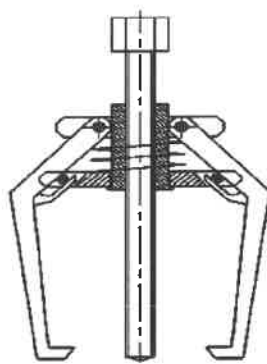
Вид предлагаемой конструкции съемного приспособления
